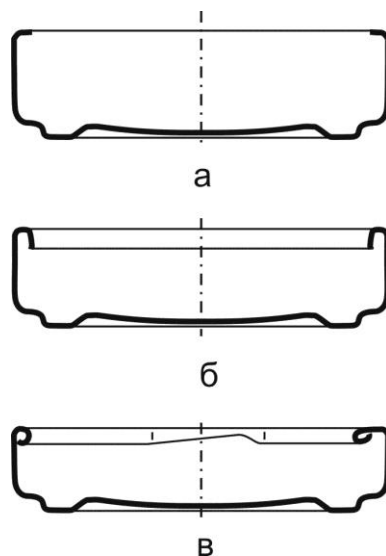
Поопераційне формування корпусу кришки з заготовки.
